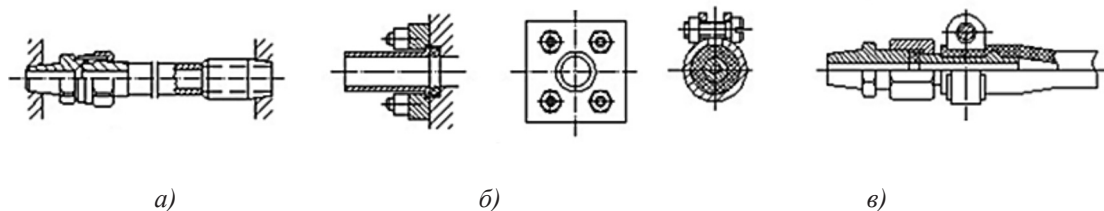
Способы соединения трубопроводов. а – с конической резьбой; б – фланцевые; в – гибких резиновых шлангов
